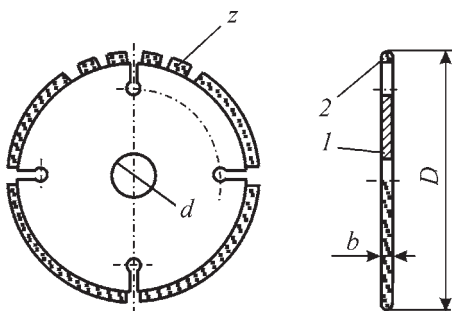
Алмазный отрезной круг с прерывистой режущей частью:
